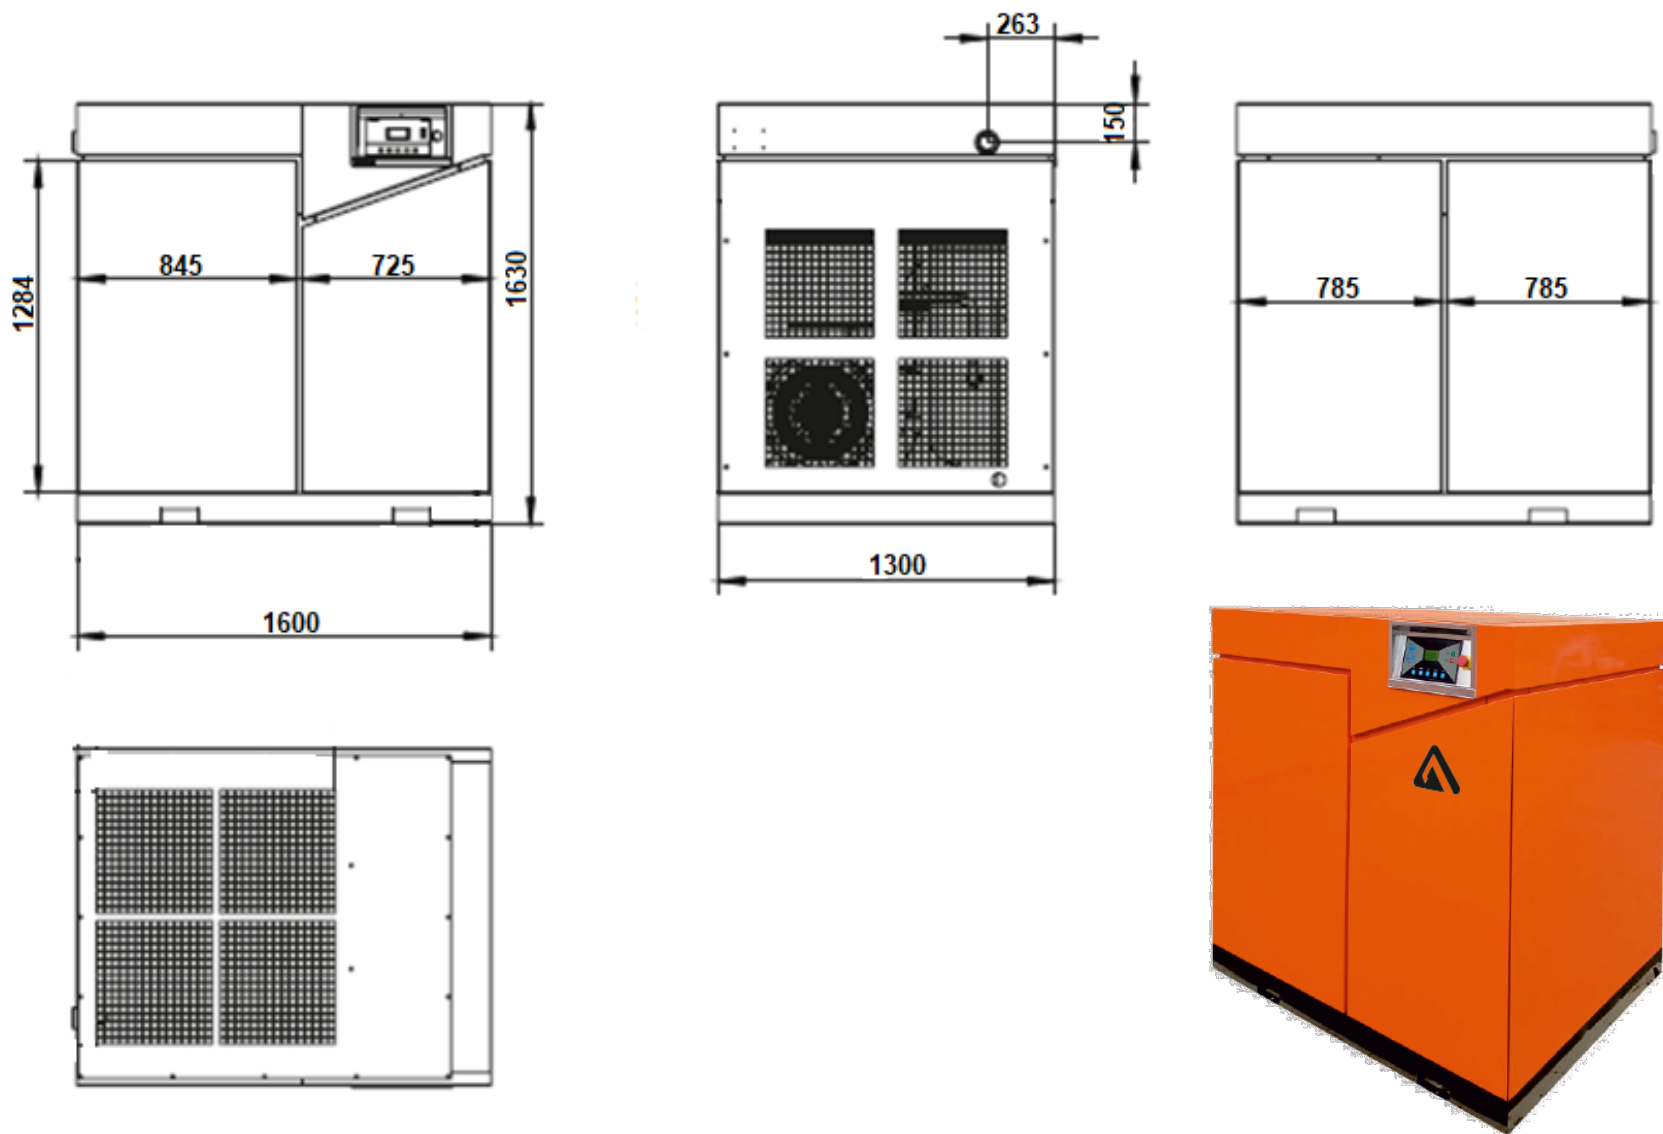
Общий вид, габаритные размеры станции компрессорной ЗИФ-СВЭ типа АРМ с двигателем 55 кВт
